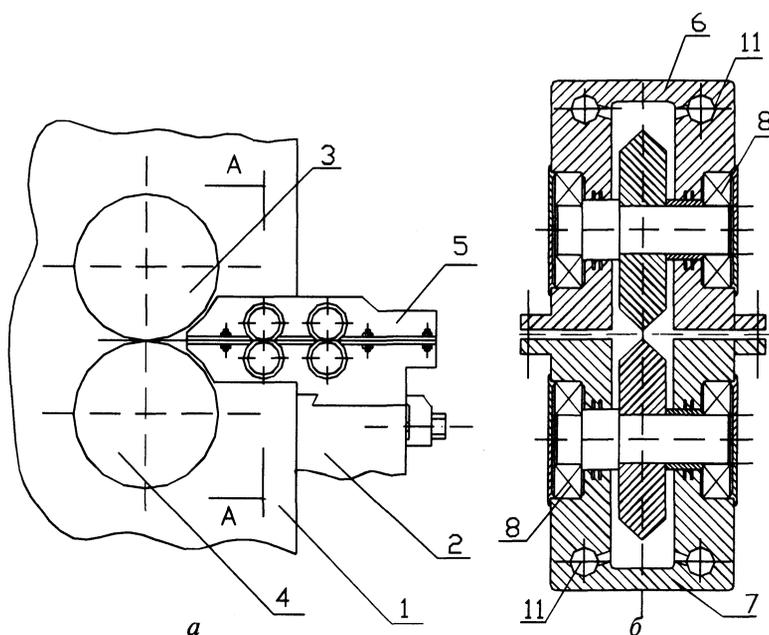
Новая концепция конструкции делительного устройства, предусматривающая использование двух пар делительных роликов: 1 – рабочая клетка с привалковым брусом; 2 – рабочие валки; 3 – корпус делительного устройства; 4, 5 – верхний и нижний элементы корпуса соответственно; 6 – фиксатор устройства; 7 – подшипник; 8 – рабочие элементы роликов; 9, 10 – основная и дополнительная пара делительных роликов
